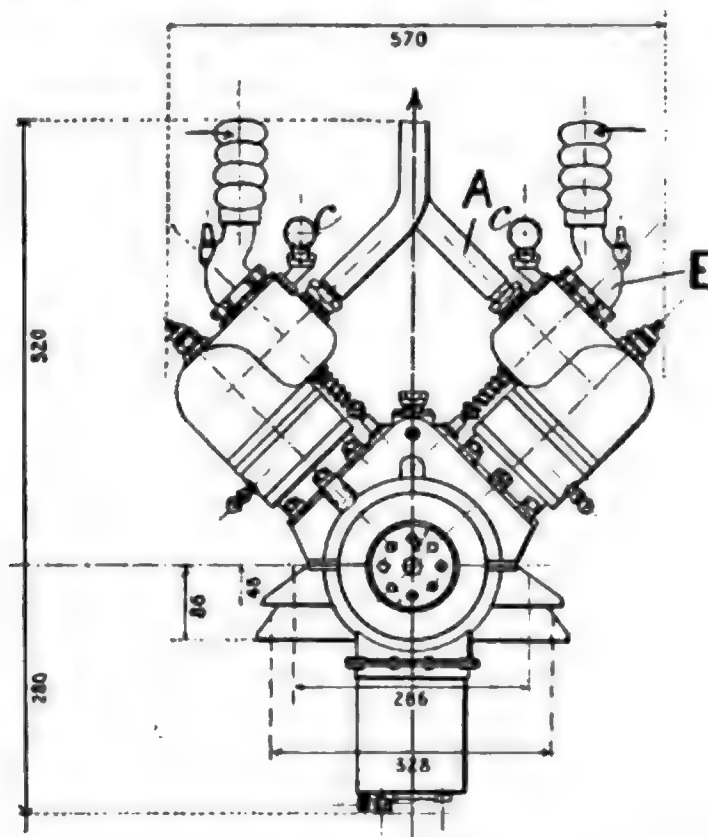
Zeichnung des Flugmotors 'Antoinette', Ansicht von vorn.
